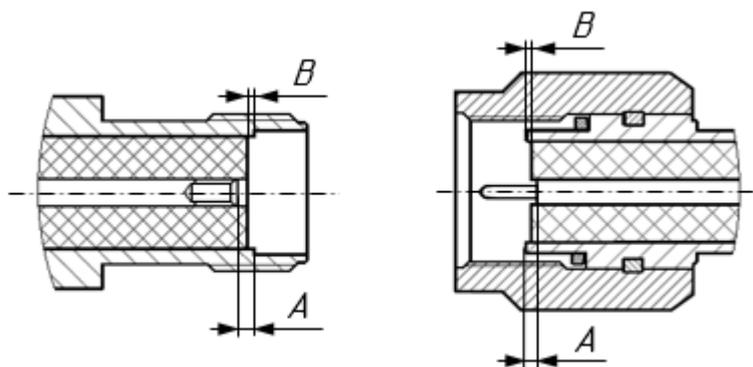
Соединители тип SMA (розетка слева, вилка справа)
